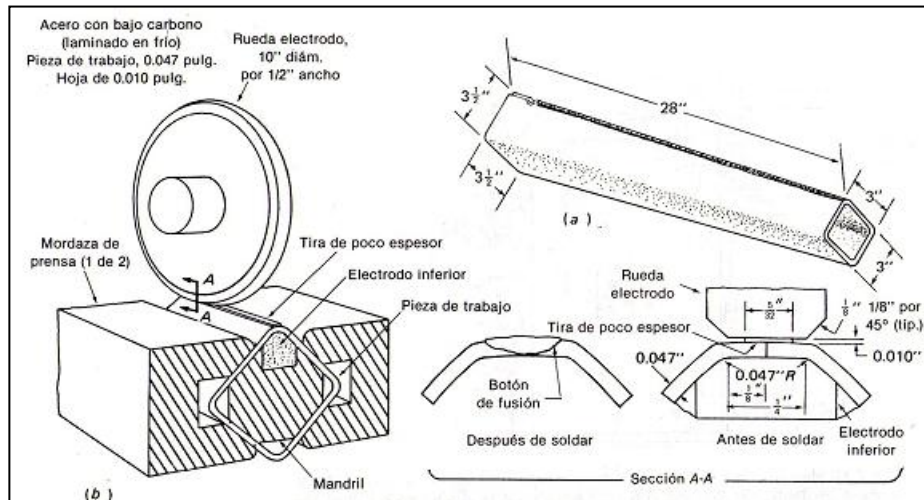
Dispositivo para soldadura de costura a tope, con rodillo, de una pata de mesa hecha de acero con bajo contenido de carbono "American Society for Metals, 1971".
